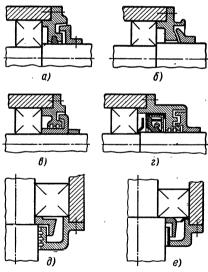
Комбинированные уплотнения: а — фетровое уплотнение в сочетании с лабиринтом; б — проточка и воротник, допускающий перекосы вала (самоустанавливающиеся подшипники); в — жировые канавки и лабиринт; г — маннетное уплотнение в сочетании с маслоотбрасывающим козырьком, жировыми канавками и лабиринтом; д, е — уплотнения для вертикальных валов, где трубка, запрессованная в крышку корпуса, образует ванну, а конус и специальная маслоотражательная шайба попают масло в полишиник
